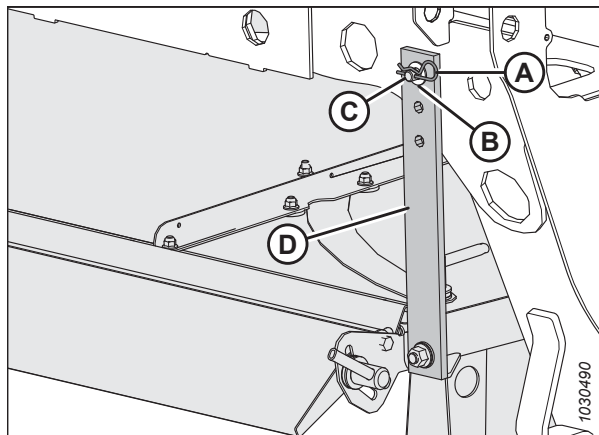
Резиновая стяжка для крепления формовочного щитка к лапе косилки
